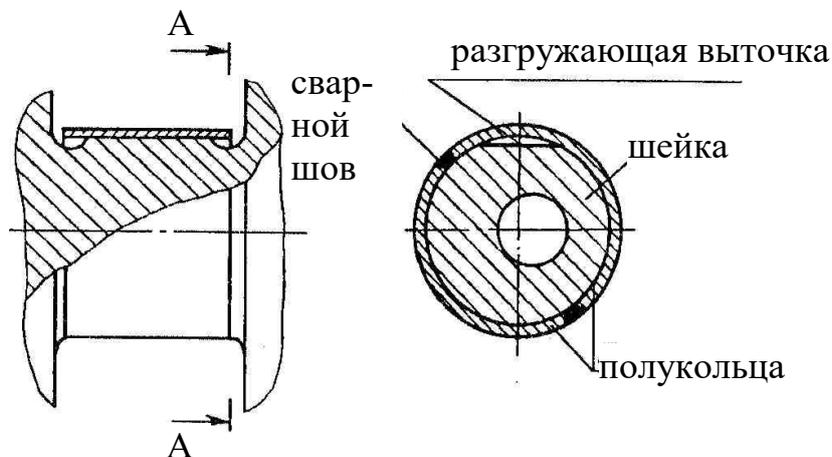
Схема восстановления шеек коленчатого вала двигателя приваркой стальных полуколец
